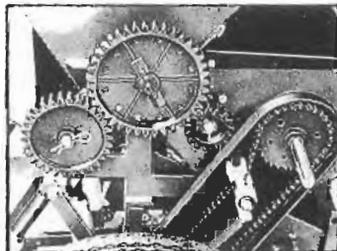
Detalle de los engranajes de transmisión de una sembradora.
